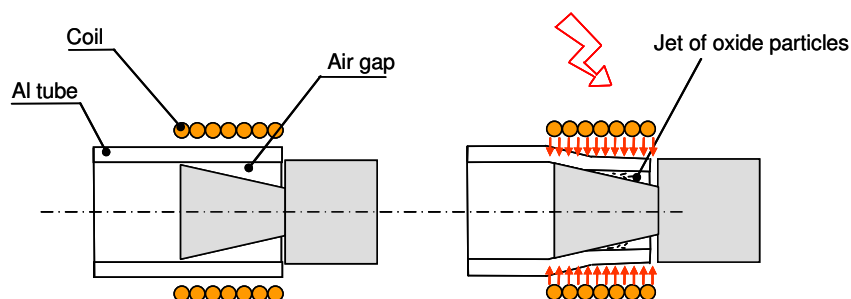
Schémas de principe du soudage par impulsion magnétique de deux tubes.
